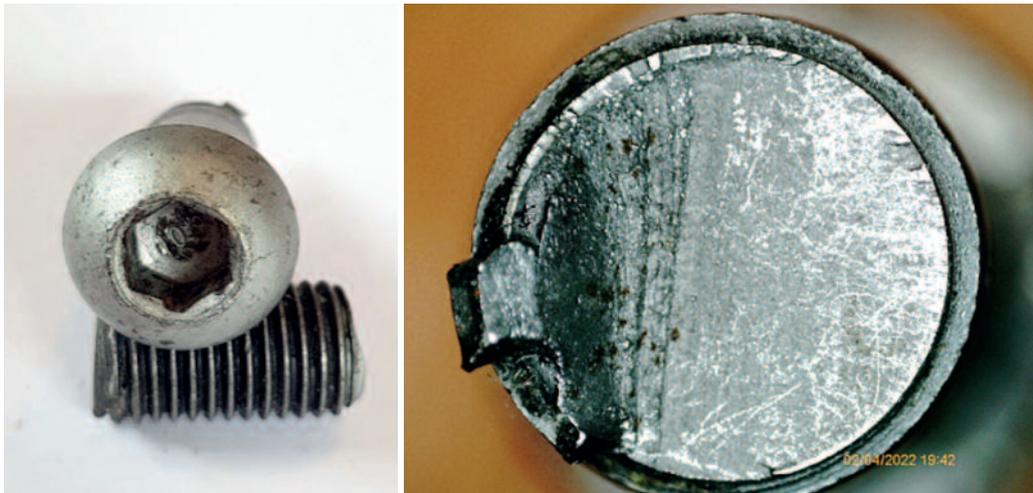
und 4: Ursprüngliche Schaftschraube M10-10.9 und deren Bruchfläche (Ermüdungsbruch beim Gewindeauslauf mit milder Kerbe und niedriger Zugspannung).
